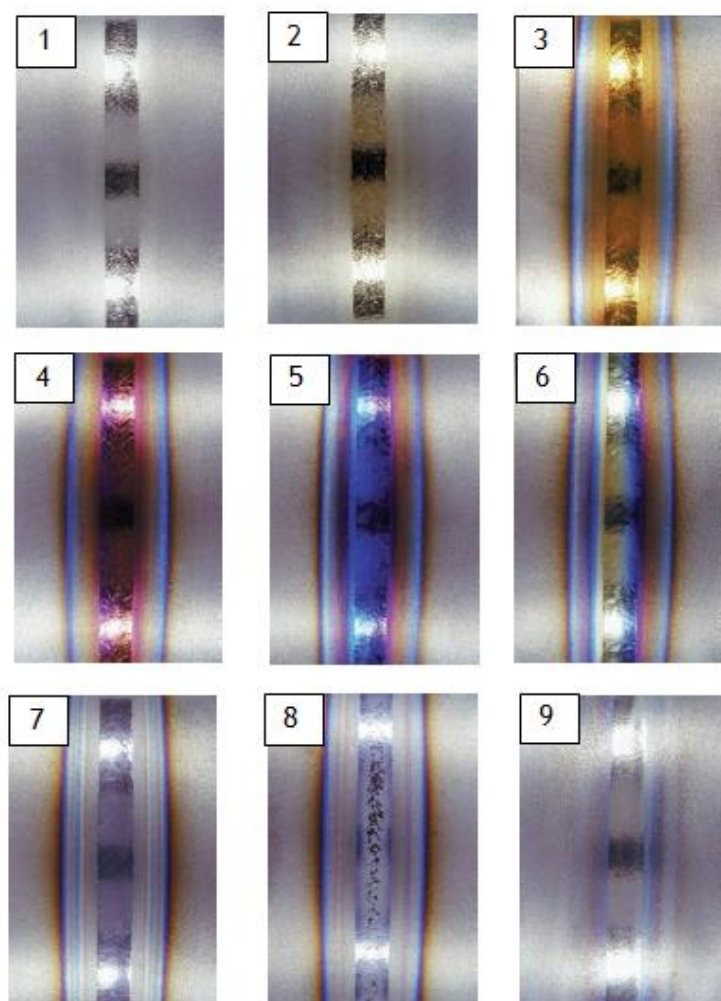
Cor dos cordões de soldadura em titânio
